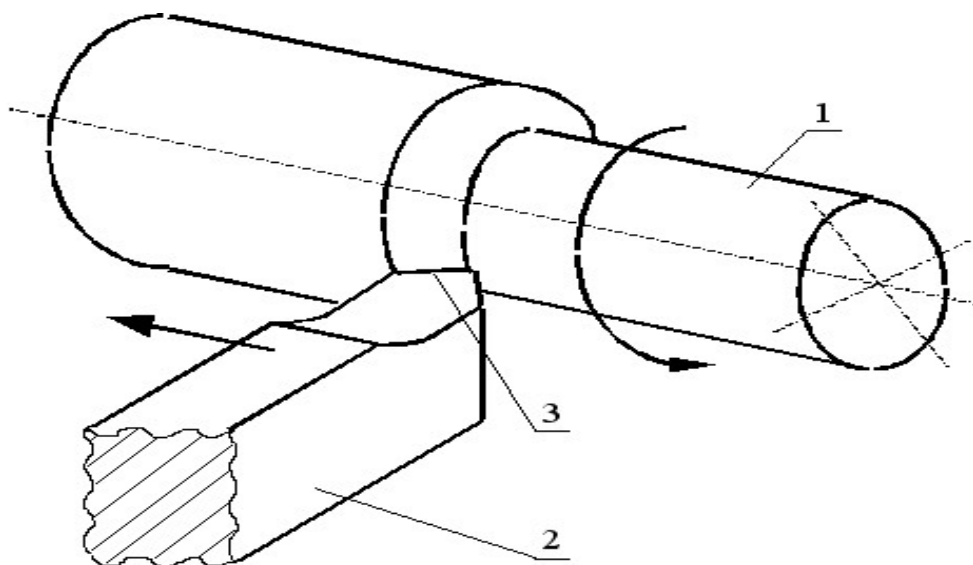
Точіння циліндричної заготовки (1) токарних прямим прохідним різцем (2); 3 – ріжуча кромка
